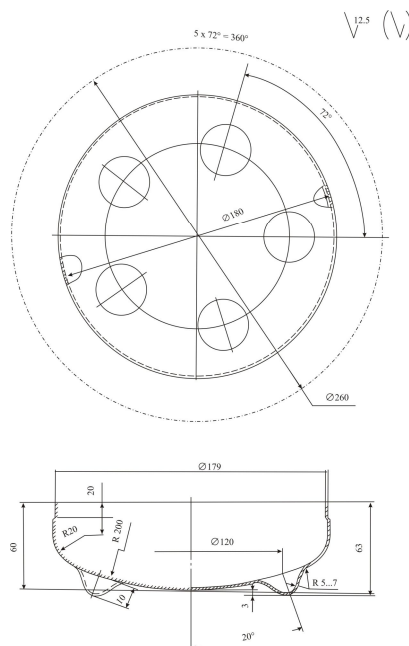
Чертеж детали «Днище нижнее» для огнетушителей типа ОП-6
